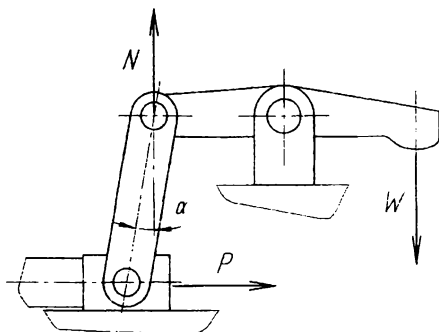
Однорычажный шарнирный зажимной механизм с ползуном
